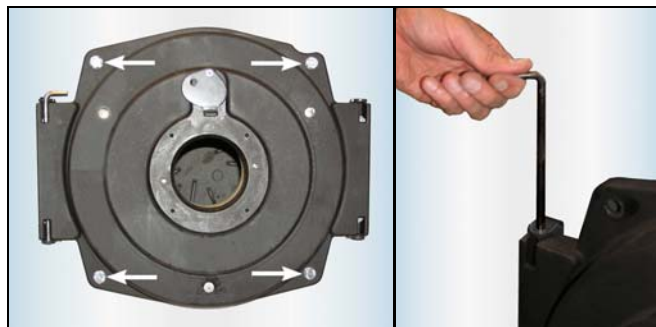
Zunächst die vier M10 Befestigungsschrauben der Kesseltür entfernen und danach die Scharnierstange nach oben herausziehen, anschließend die Kesseltür demontieren.
